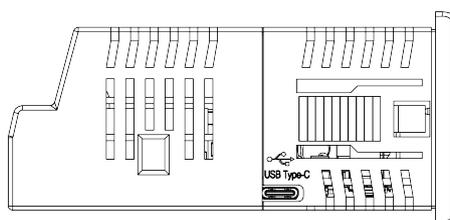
Расположение разъема USB для корпуса Щ2
